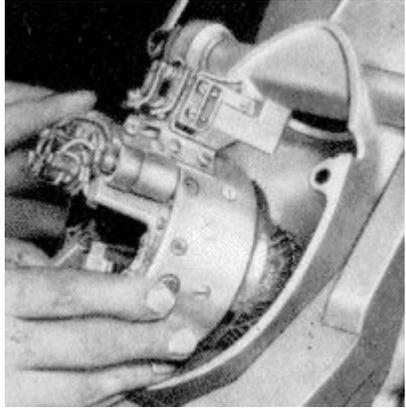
Ausbau der Lichtmaschinenhaltekappe
